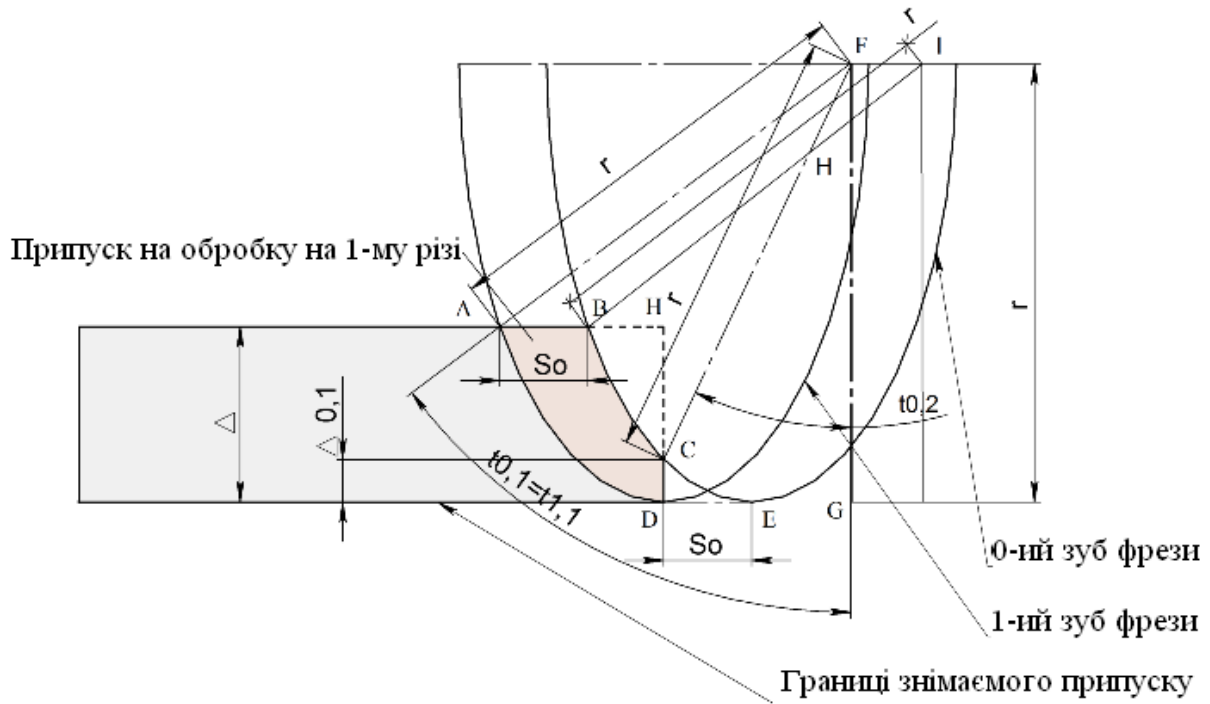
Схема двухпараметричного адаптивного керування процесом швидкісного зубофрезерування ЗКЗК
